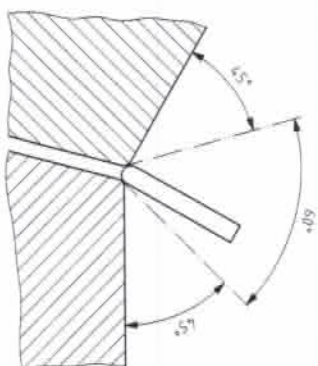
Bewegung des Rundstabs mit 8 mm Durchmesser
